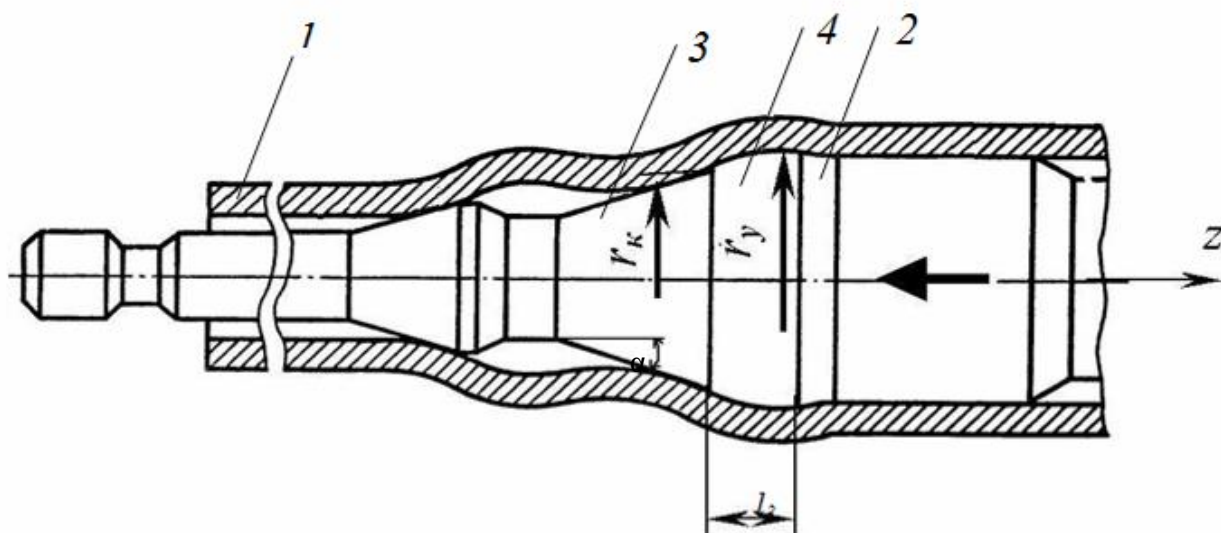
Схема обробки отвору заготовки групою елементів, останній з яких має додаткову криволінійну ділянку: 1 - заготовка, 2 - деформуючий елемент, 3 - робочий конус, 4 - додаткова ділянка
